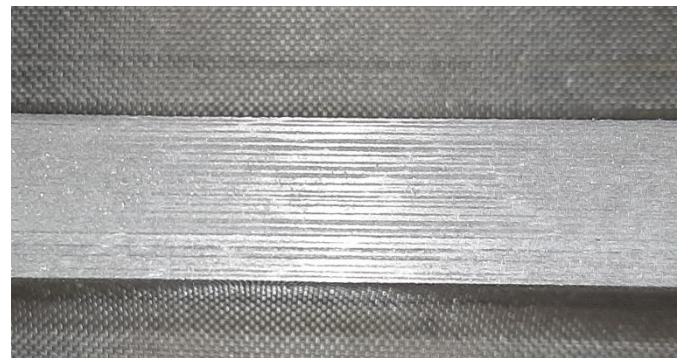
Сколы и вырыв ленты после фрезерования твердосплавным роутером
